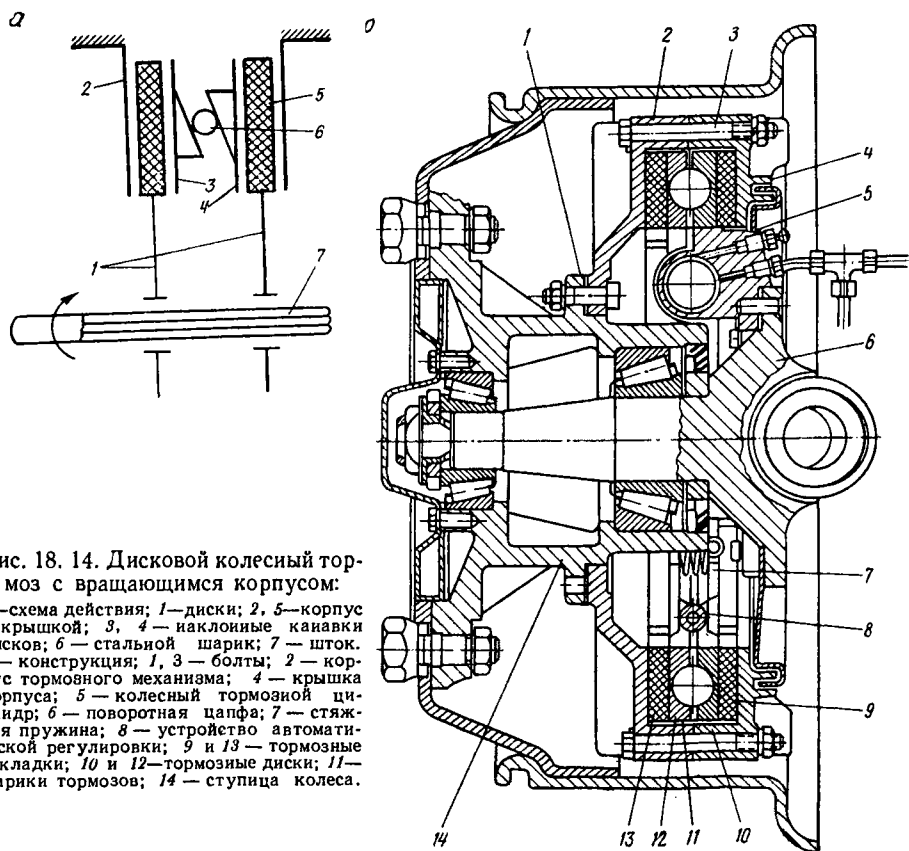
14. Дисковой колесный тормоз с вращающимся корпусом:
